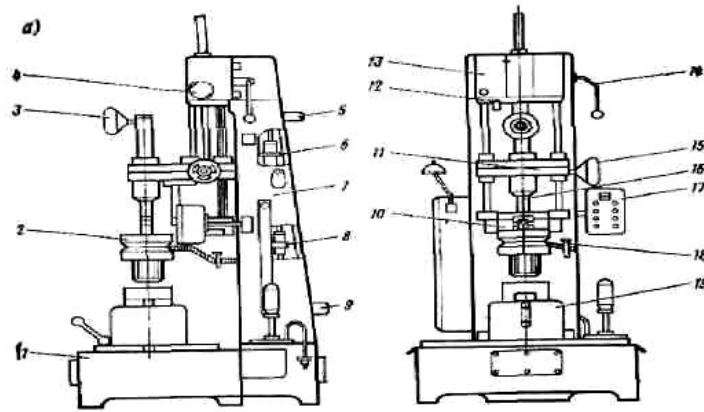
Хонінгувальний станок ЗГ833: а - пристрій: 1 - станина; 2 - шпіндель; 3 - маховик механізму розтиску хону; 4 - кулачки регулювання ходу повзуна; 5 - електродвигун зворотно - поступальної ходи шпінделя; 6 - привід зворотно - поступальної ходи хонінгувальної головки; 7 - колона; 8 - привід обертання шпінделя; 9 - електродвигун приводу обертання шпінделя; 10 - редуктор; 11 - повзун; 12 - штовхач кінцевого вимикача; 13 - коробка подач; 14 - рукоятка реверсу; 15 - маховик ручного введення хону; 16 - повідець хонінгувальної головки; 17 - пульт управління; 18 - кран охолодження; 19 - пристосування для обробки гільз або блоків
